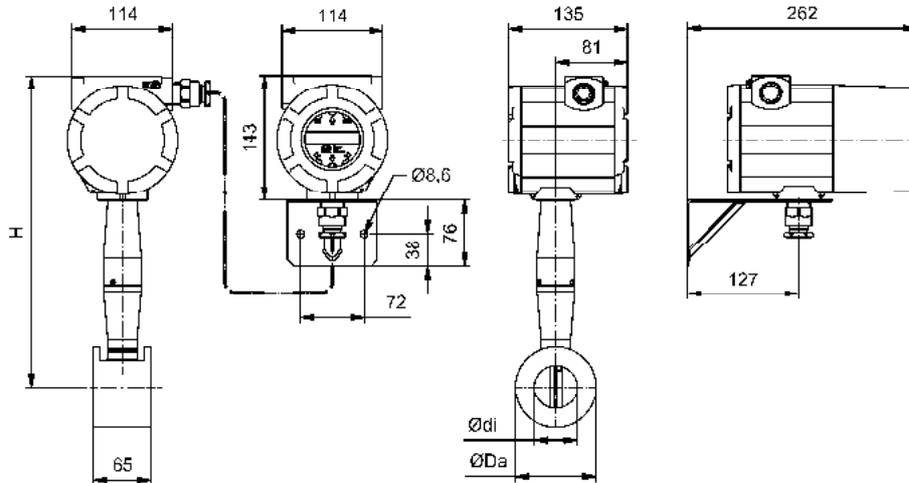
Dimensionen Zwischenflansch mit separater Elektronik
